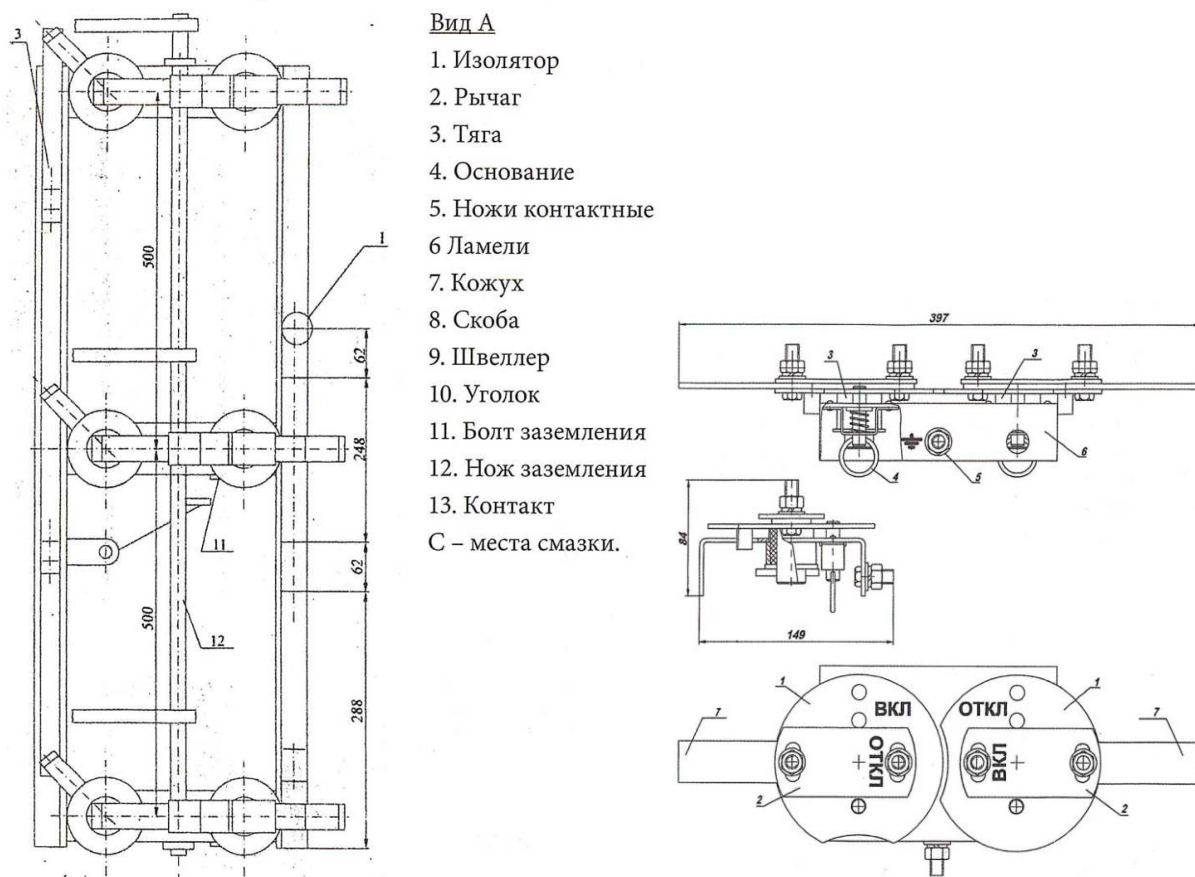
Общий вид, габаритные, установочные и присоединительные размеры разъединителя и привода.
